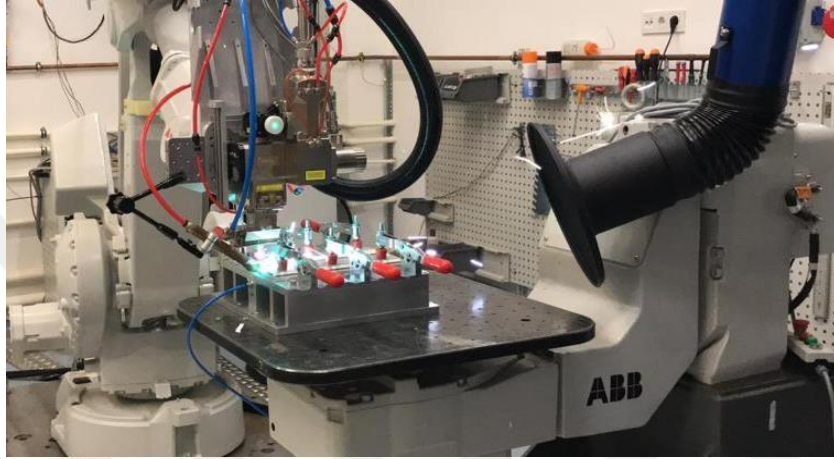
Lazer kaynak makinesi ve ekipmanları
